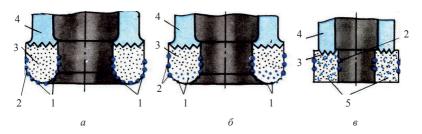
Типы алмазных коронок: a – однослойная; δ – многослойная; s – импрегнированная; 1 – объёмные алмазы; 2 – подрезные алмазы; 3 – матрица; 4 – корпус коронки; 5 – матрица, насыщенная мелкими алмазами
